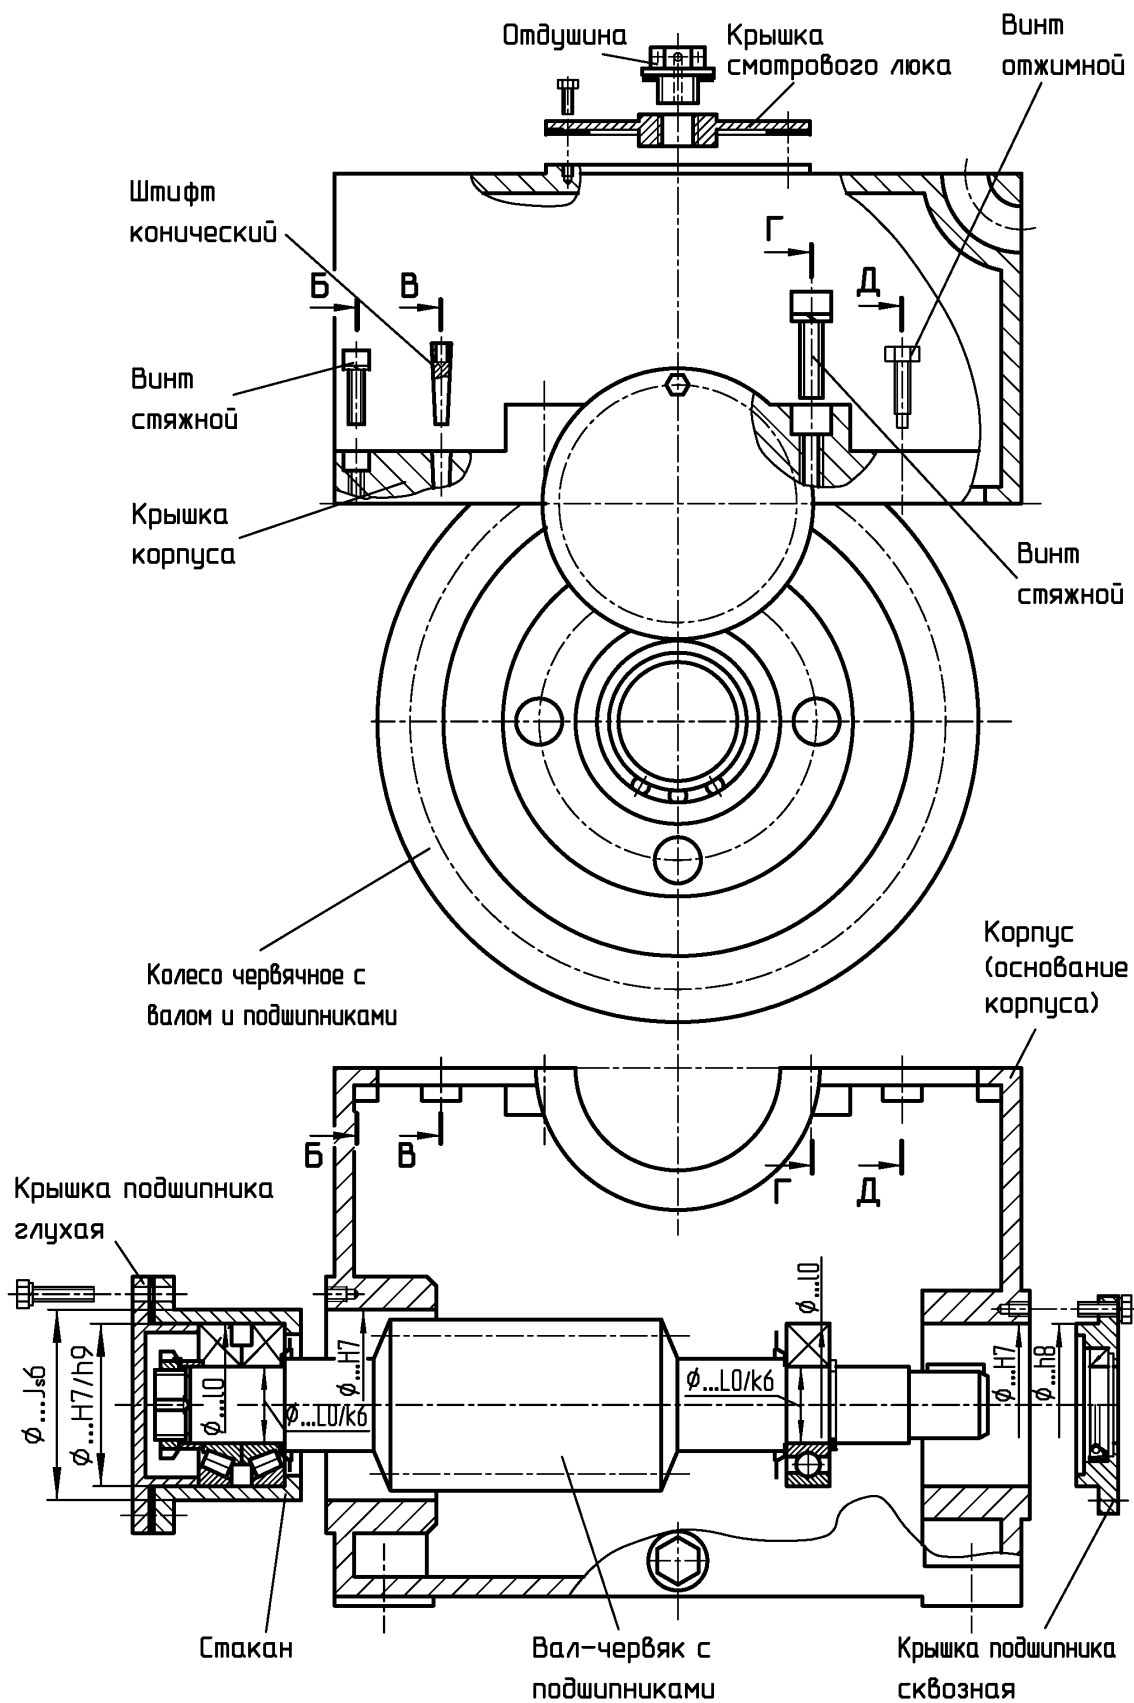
Конструкция червячного редуктора с разъемным корпусом
